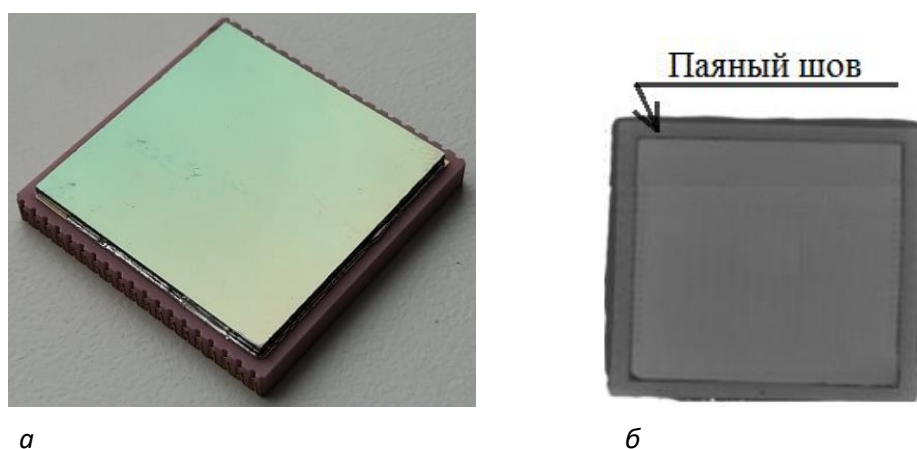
Внешний вид загерметизированного корпуса микроболометра
